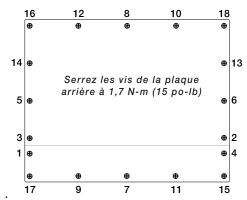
Plaque arrière de boîtier d'indicateur 820i et 920i
